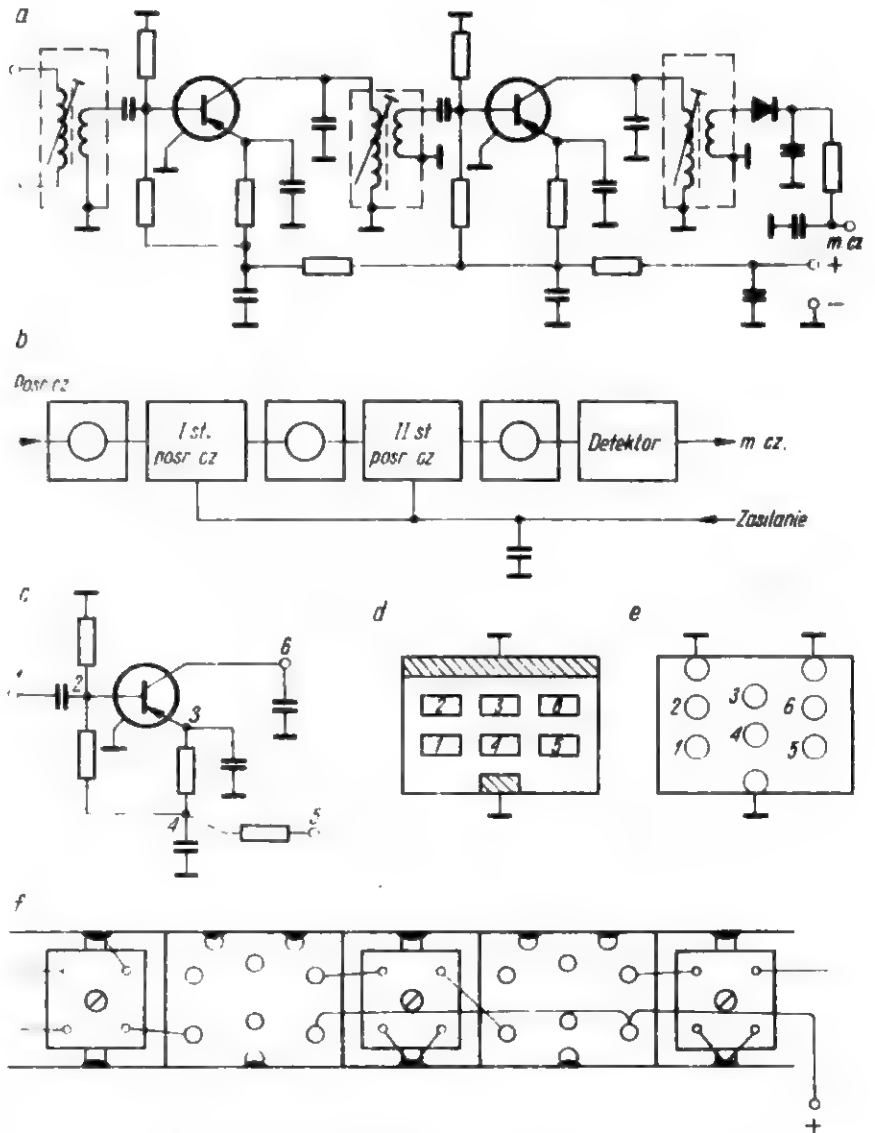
Przykład konstrukcji wsporczej (ramki) dla modułów
